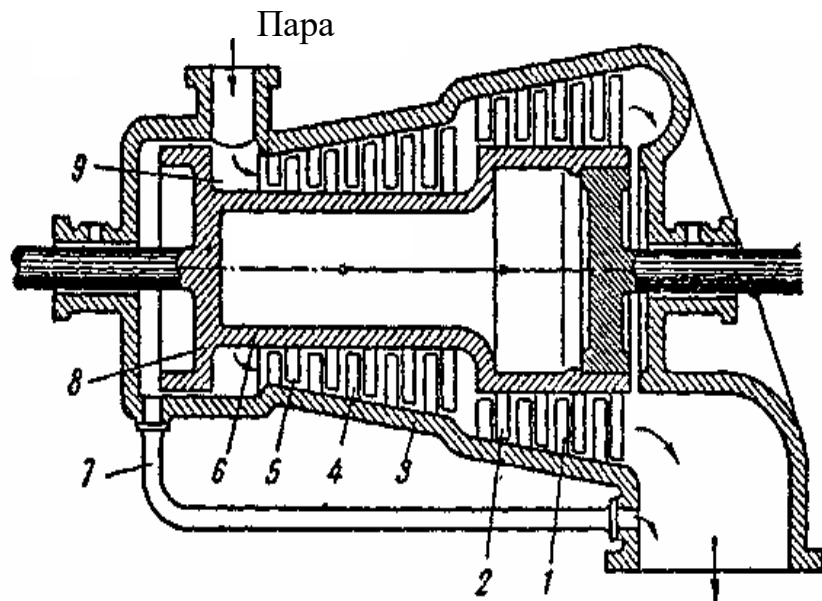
Схема реактивної турбіни Парсонса: 1 і 4 – напрямні лопаті; 2 і 5 – робочі лопаті; 3 – корпус; 6 – ротор; 7 – паропровід; 8 – розвантажувальний поршень
